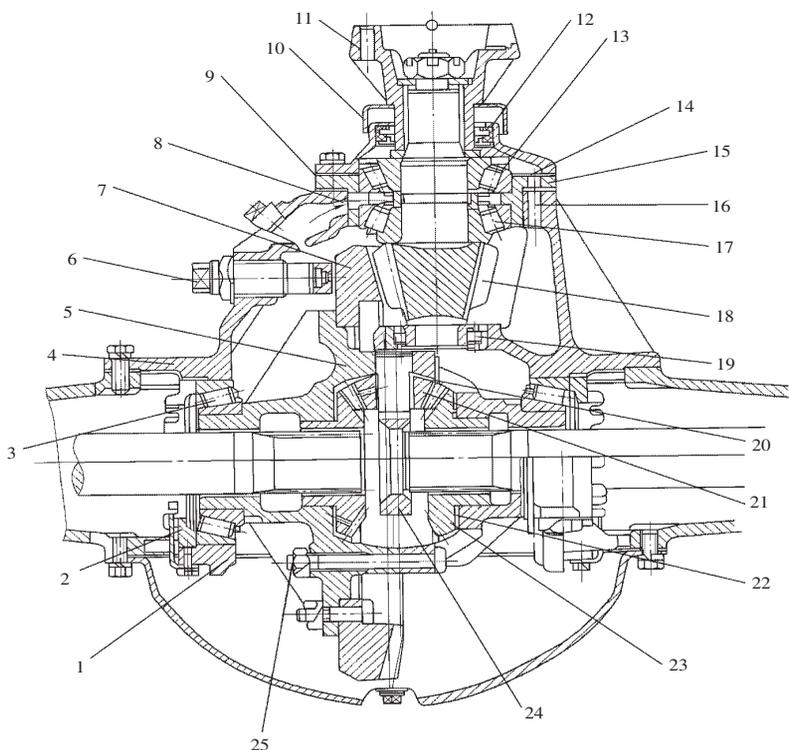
东风 EQ1090 型汽车单级主减速器及差速器
